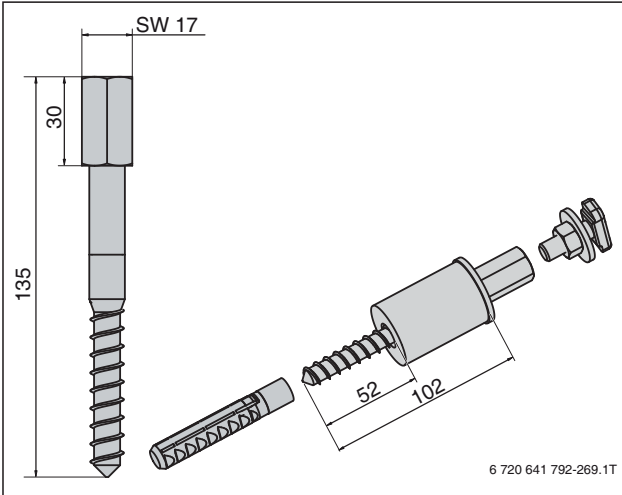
Stockschraube für die Flachdachmontage von SKR21
